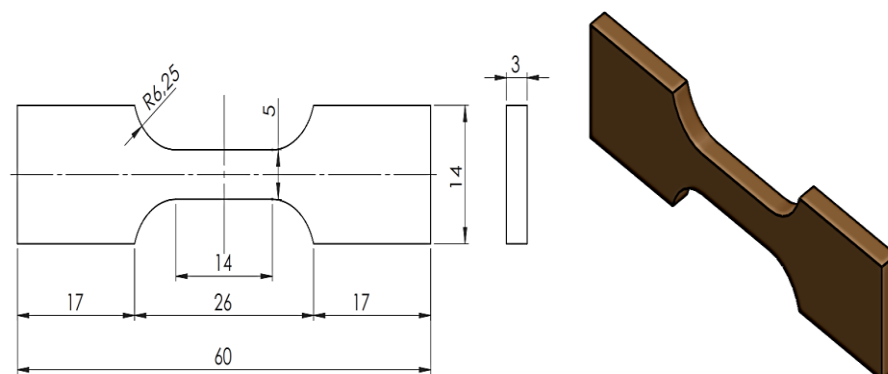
Desenho técnico do corpo de prova de tração. Fonte: Autor.
